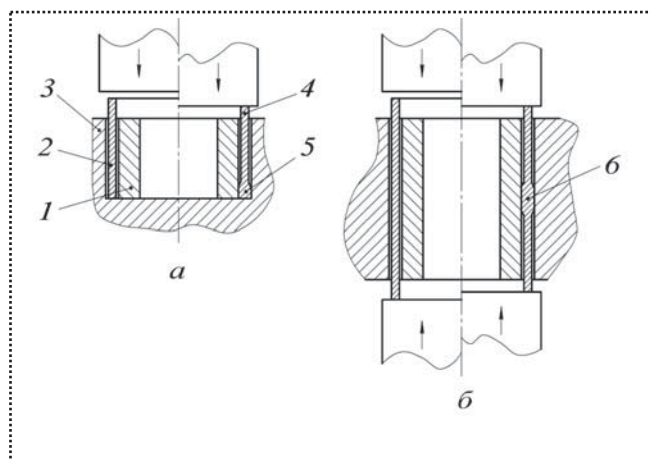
Сборка прессового соединения с промежуточной втулкой
